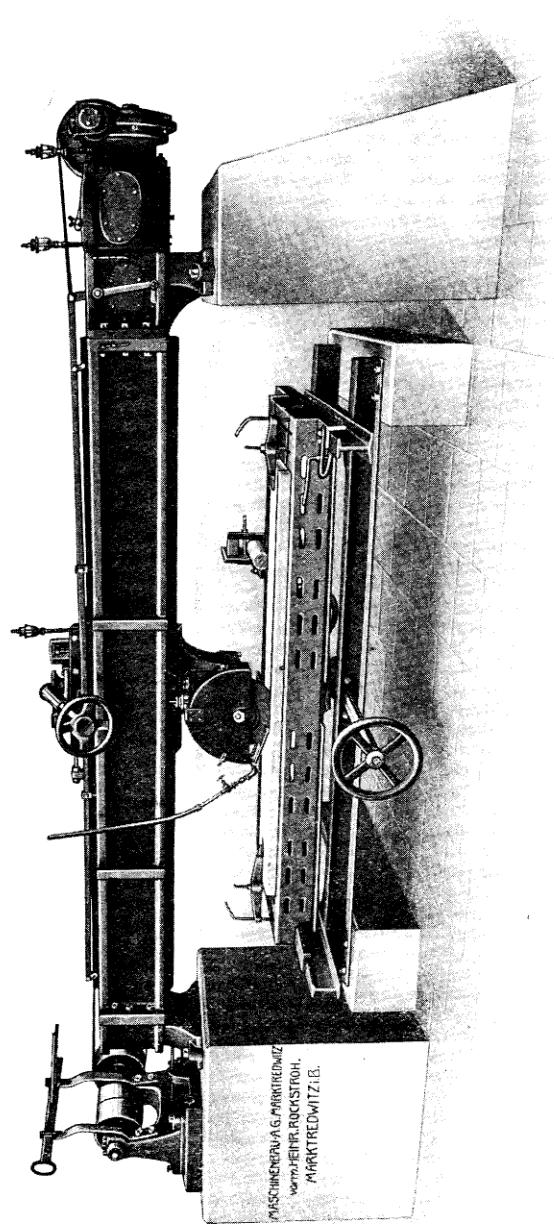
Machine à scier et à fraiser le marbre et le granit.
